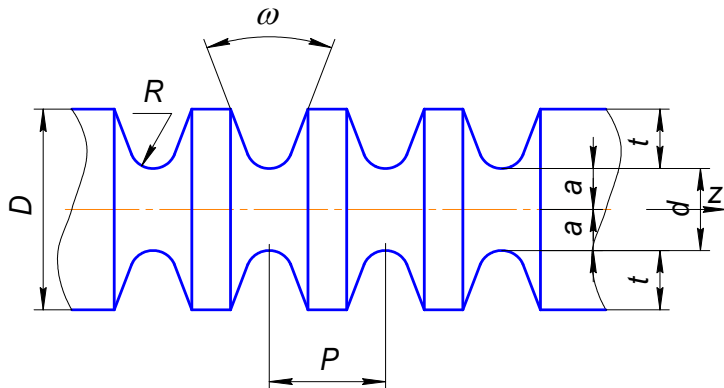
Цилиндрический образец с надрезами V-образного профиля
